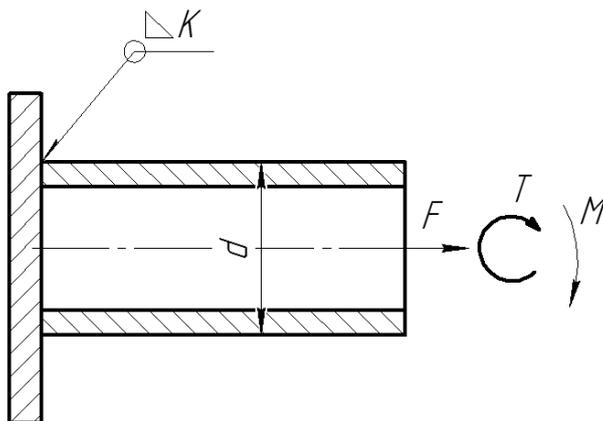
Схема таврового соединения трубы с плитой угловым швом
